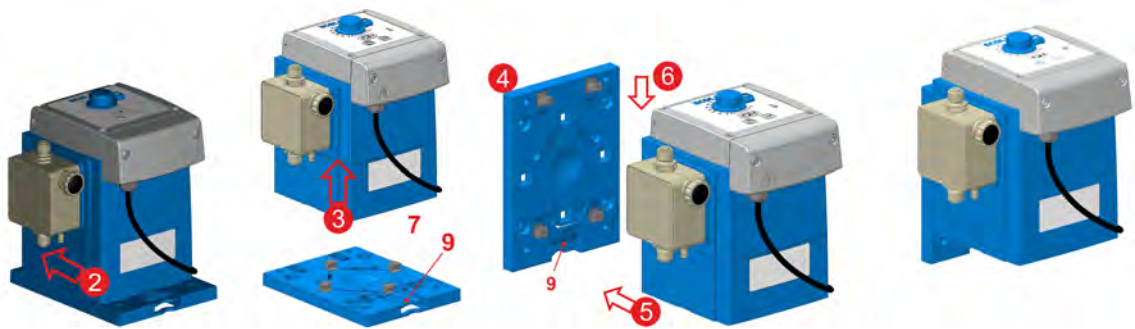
Cambio de montaje en mesa (de pie) a montaje en pared (suspendida)
